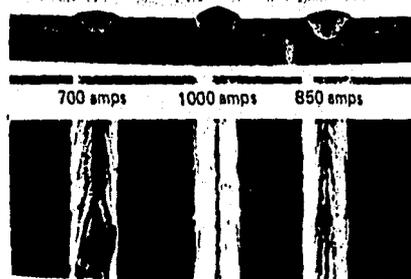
Efecto de los niveles de corriente en soldadura. La penetración y la fusión unitaria crecen con el aumento de la corriente
